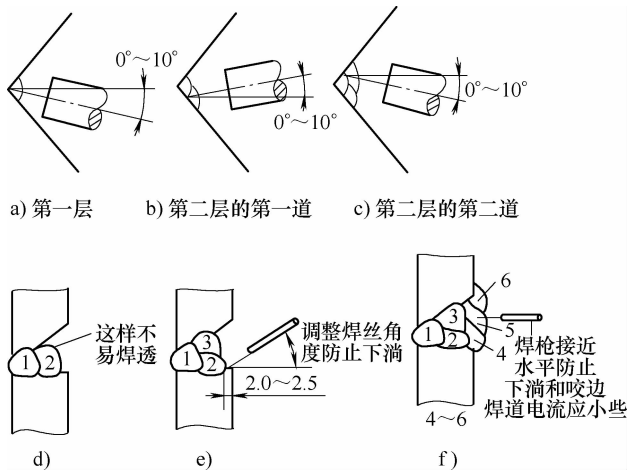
多层横焊时的焊枪姿势和焊道的排列方式
